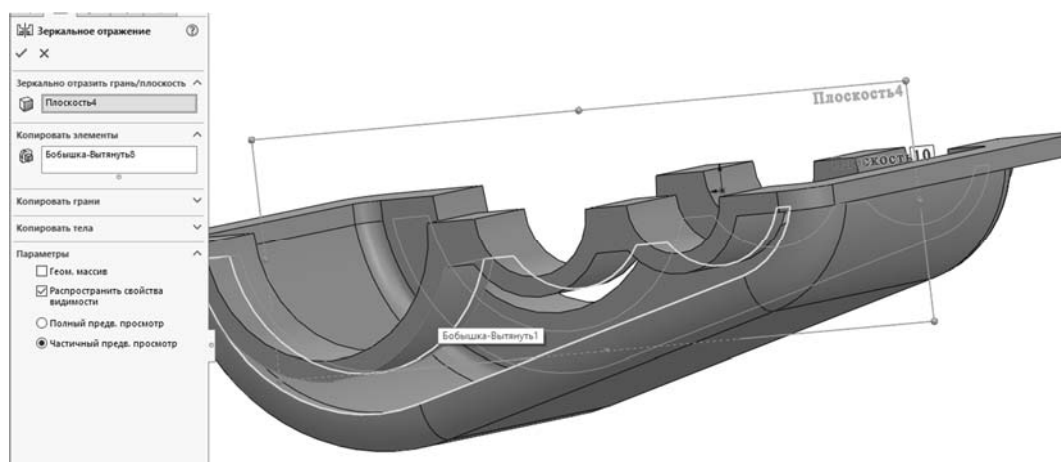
Изображение 3D-модели крышки редуктора
